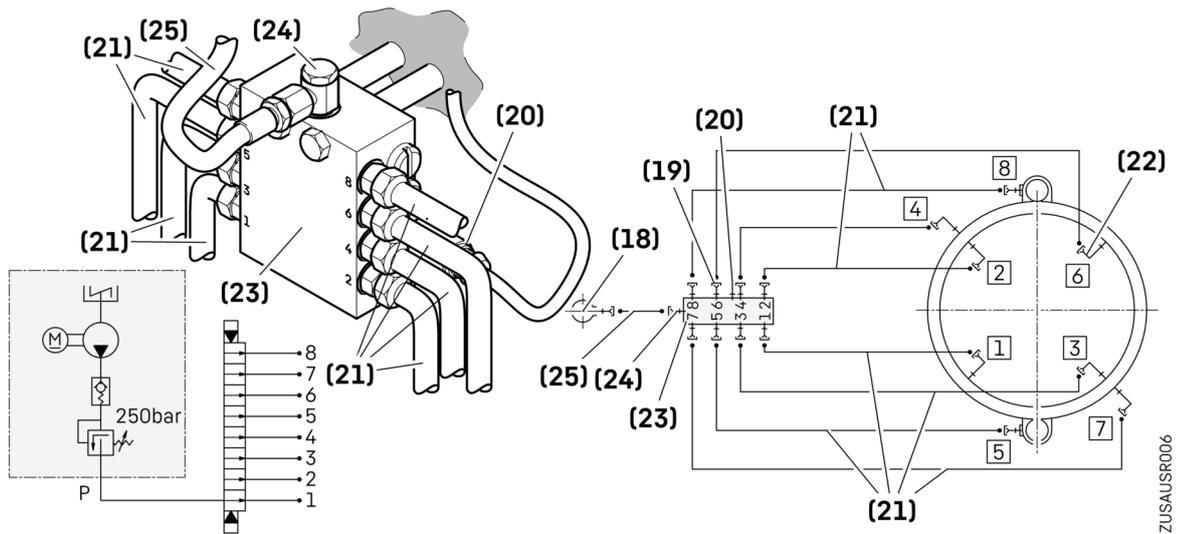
Verlegeplan und Hydraulik-Schaltplan (8er-Verteiler mit zwei Drehwerken)
